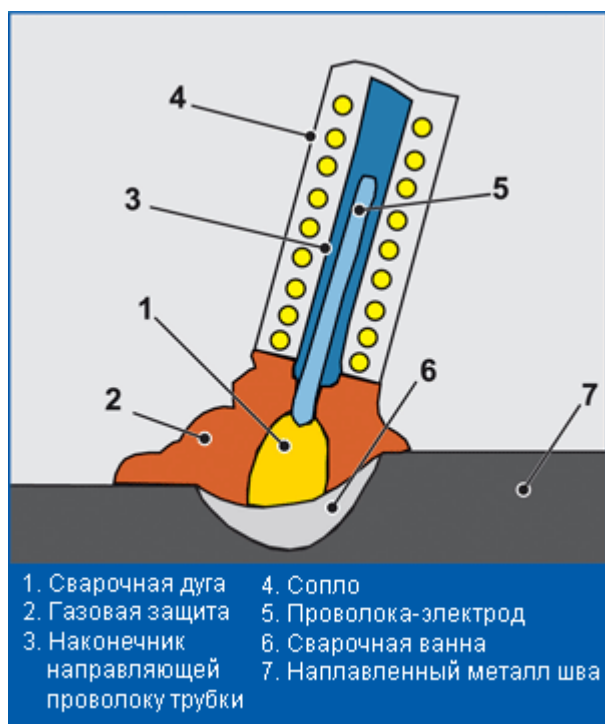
Полуавтоматическая сварка электродной проволокой в среде защитного газа - инертного (аргона) или активного (углекислого газа)
